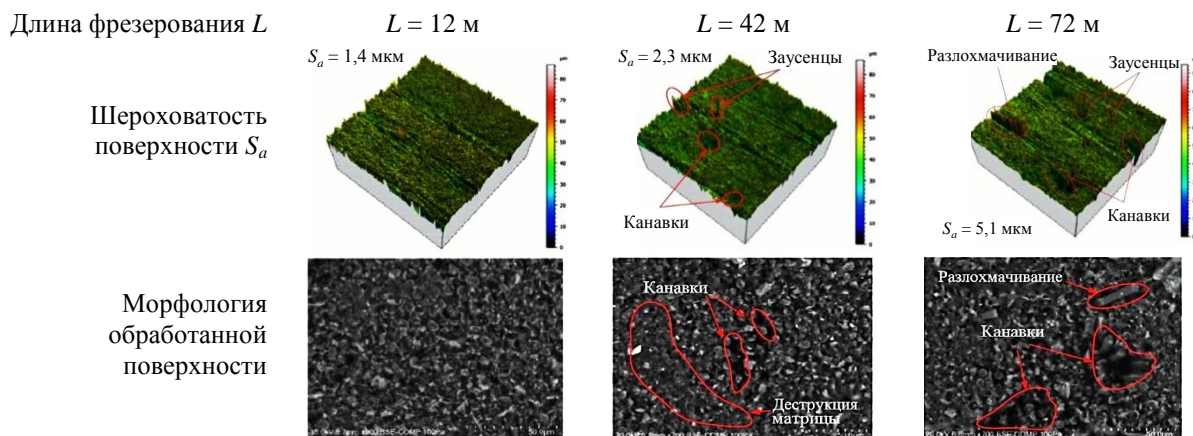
Морфология и шероховатость поверхности углепластика на разной длине фрезерования
